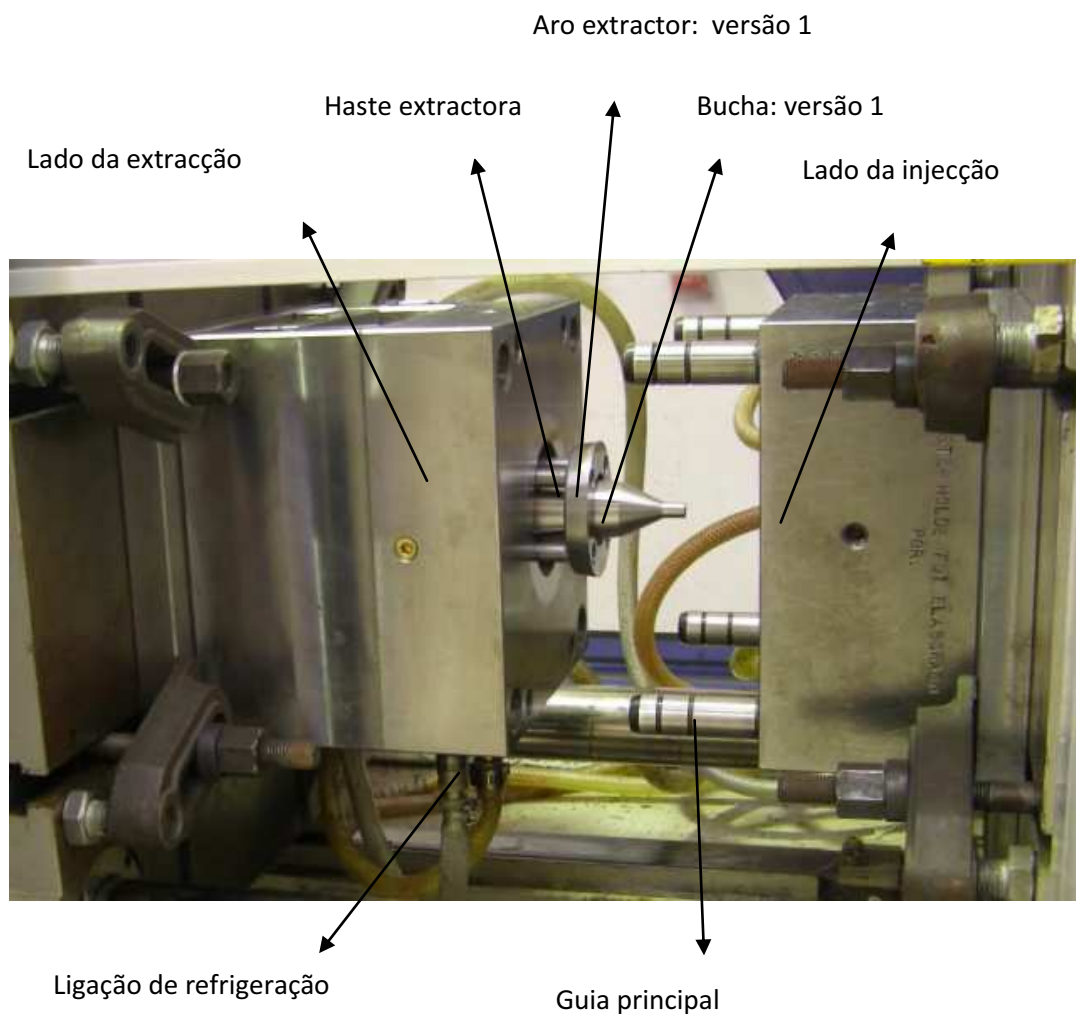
Molde montado na máquina de injeção: versão 1 [3 corpos]
